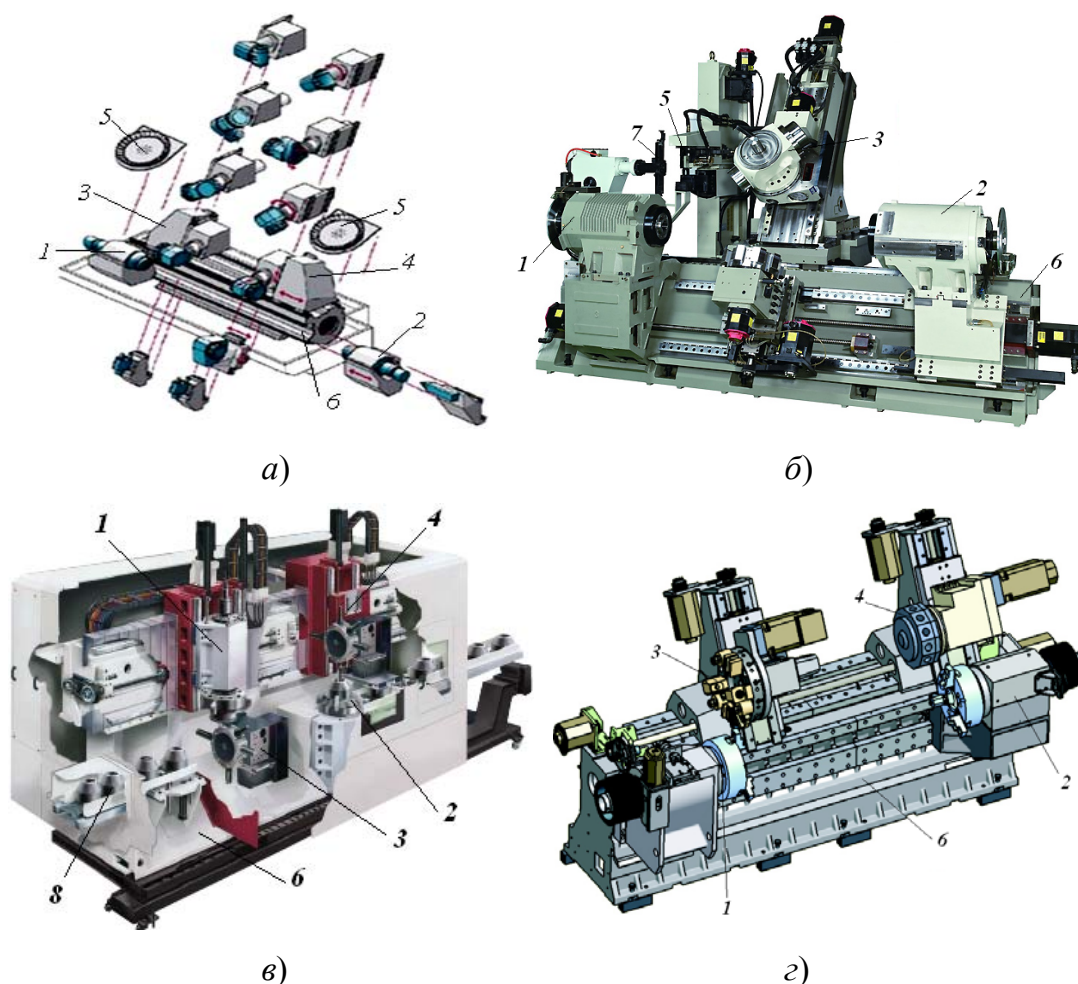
Компоновки токарных станков с ЧПУ:
